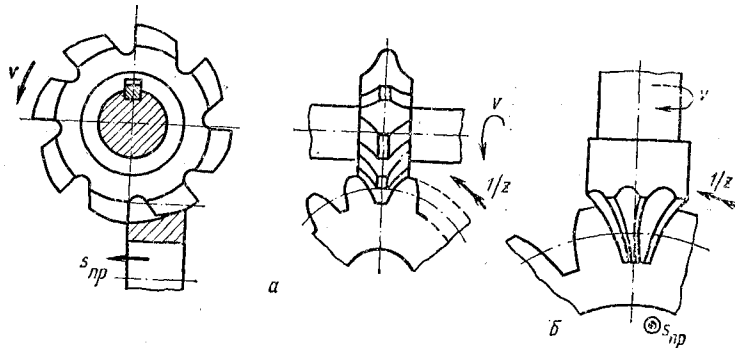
Схемы фрезерования зубьев зубчатых колес методом копирования
